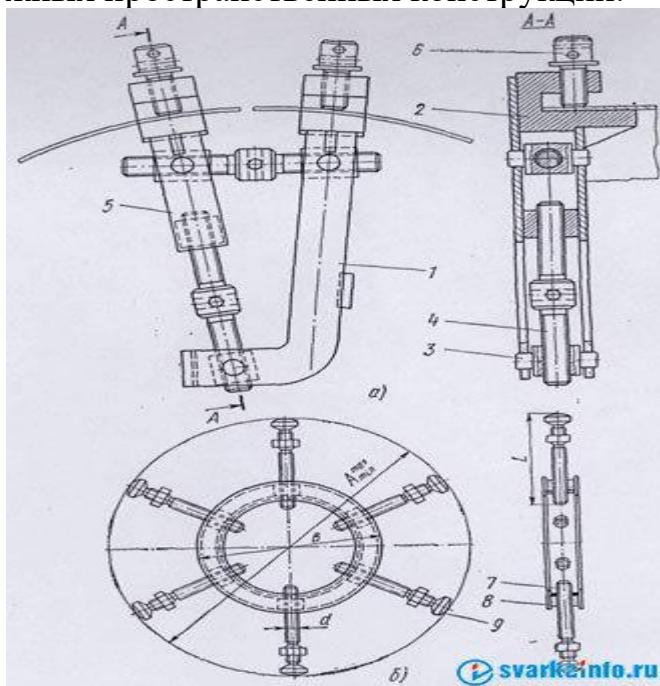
Стягивающее (а) и распорное (б) приспособления:
